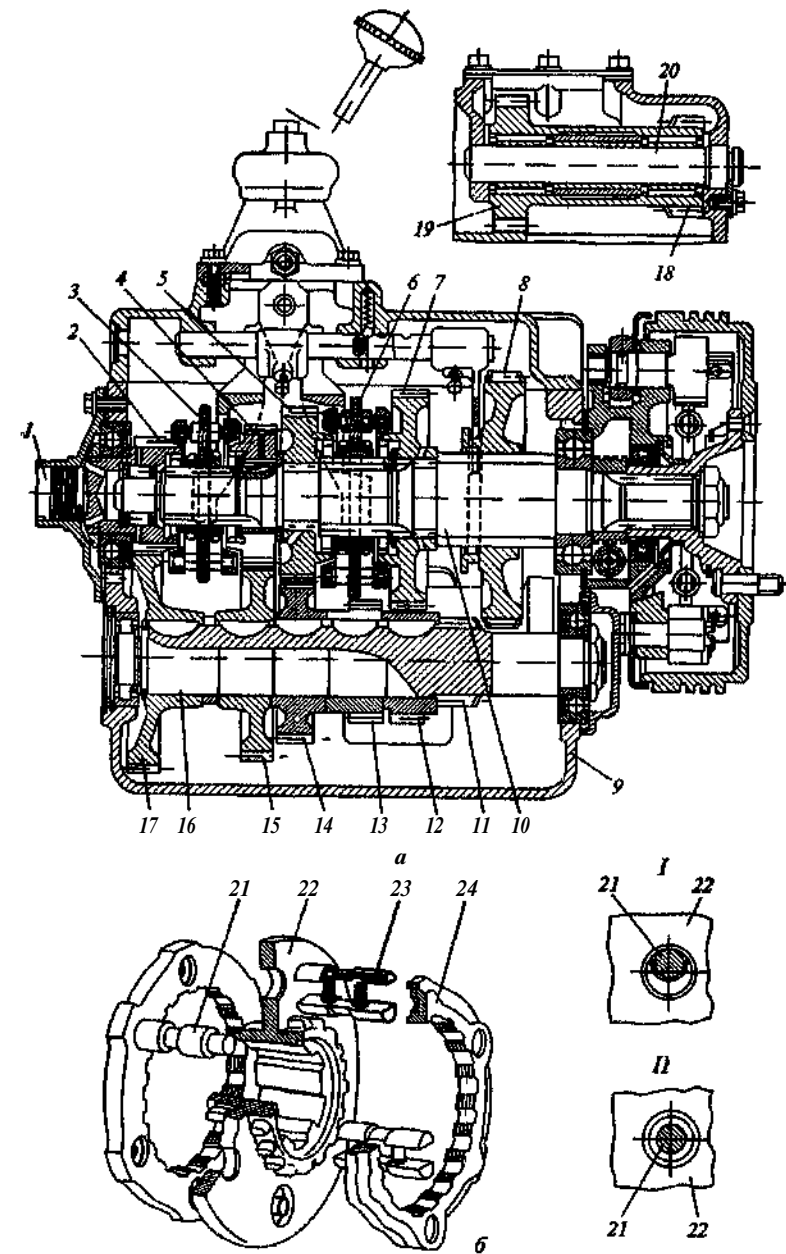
Коробка передач грузового автомобиля ЗИЛ:
